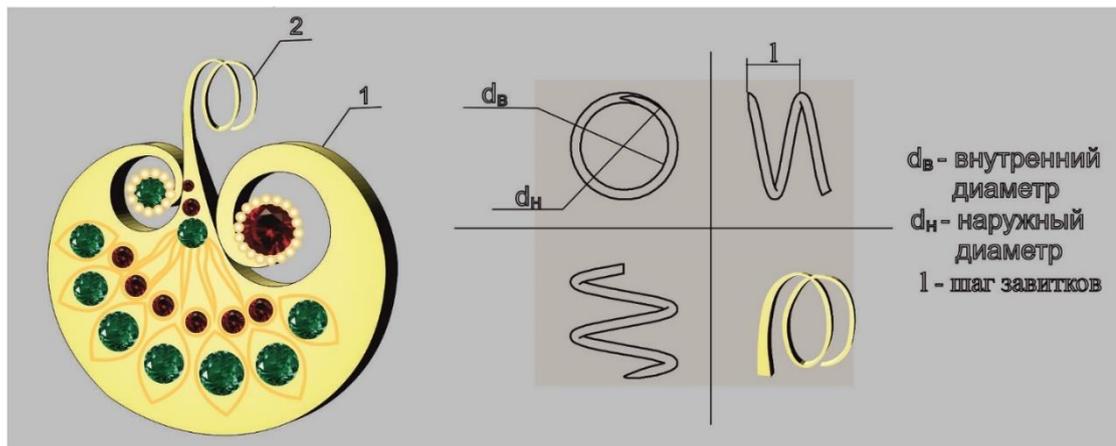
Общий вид серьги и чертеж швензы-спирали
